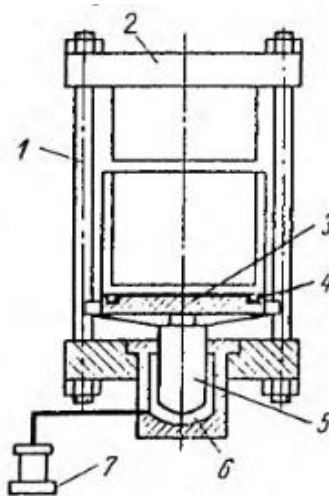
Схема гідравлічного преса: 1 – колона; 2 – нерухома плита; 3 –плита-траверса; 4 – чашка; 5 – плунжер; 6 – циліндр; 7 – насос
